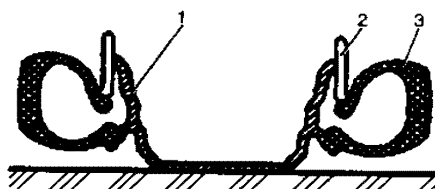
Схема накачки бескамерной шины с помощью уплотняющего кольца
